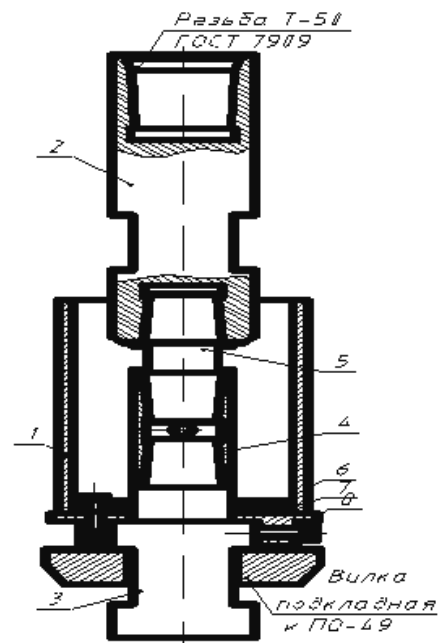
Приставка к стенду для определения средней наработки замковой резьбы на отказ: 1 – стакан; 2 – удлинитель; 3 – опора нижняя; 4 – муфта; 5 – ниппель; 6 – диск; 7 – прокладка; 8 – болты; 9 – гайки
